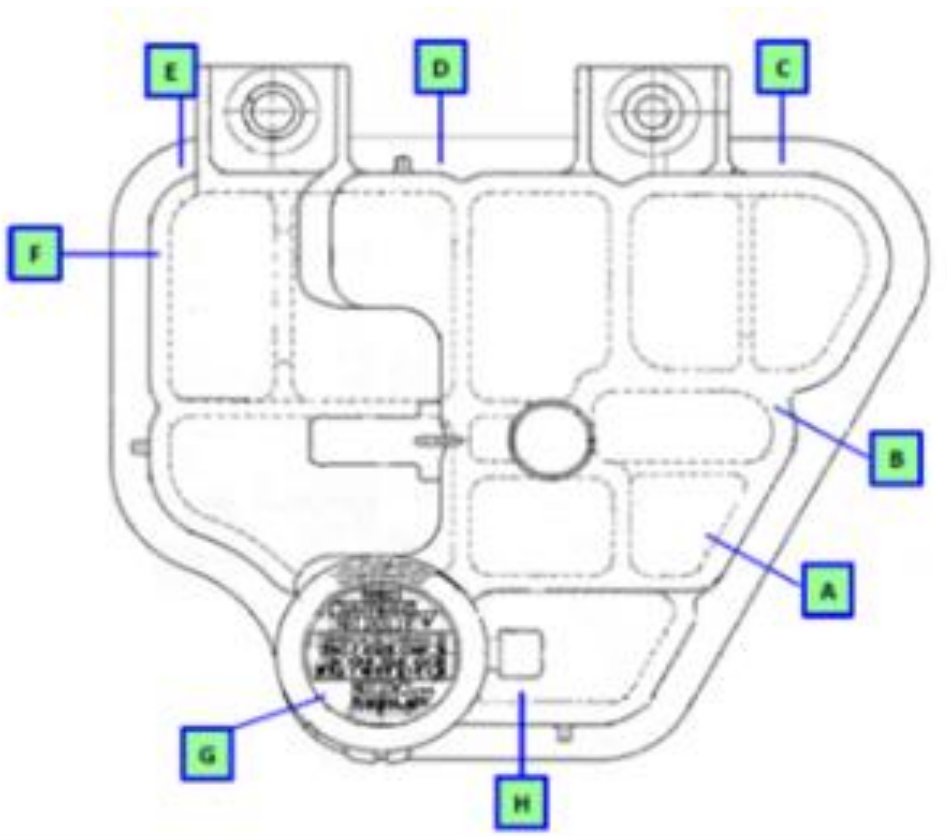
Puntos de medición de alineación y altura de soldadura
